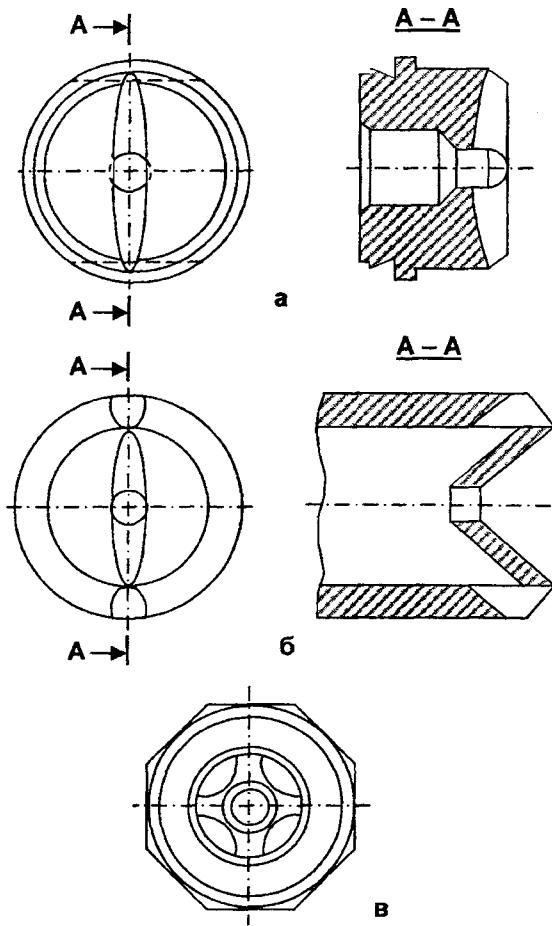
Схемы форсунок для водяного охлаждения заготовки:
